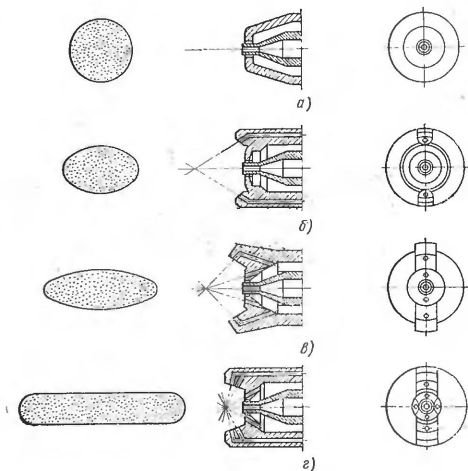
Распылительные головки краскораспылителей и отпечатки их факелов: *а*—головка без дополнительных отверстий, *б*—головка с двумя дополнительными боковыми отверстиями; *в*—головка с четырьмя дополнительными отверстиями; *г*—головка с восемью дополнительными отверстиями
